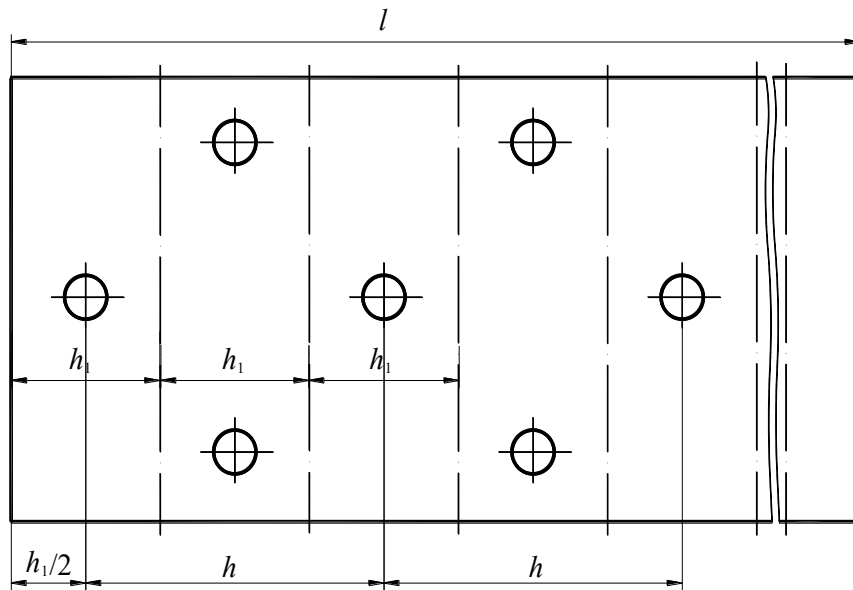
Схема частичной развёртки колкового барабана с рабочей длиной ℓ и рядами колков
